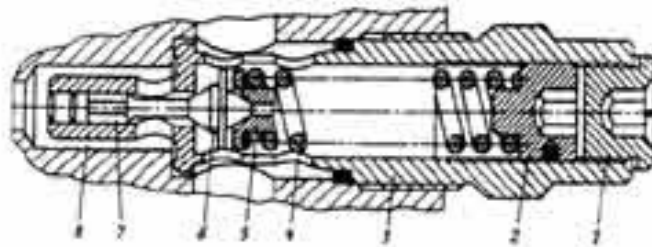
Предохранительный клапан прямого действия 1 - пробка; 2 - регулировочный винт; 3 - корпус; 4 - пружина; 5 - направляющая втулка; 6 - запорно-регулирующий элемент; 7 - демпфер; 8 – седло.
